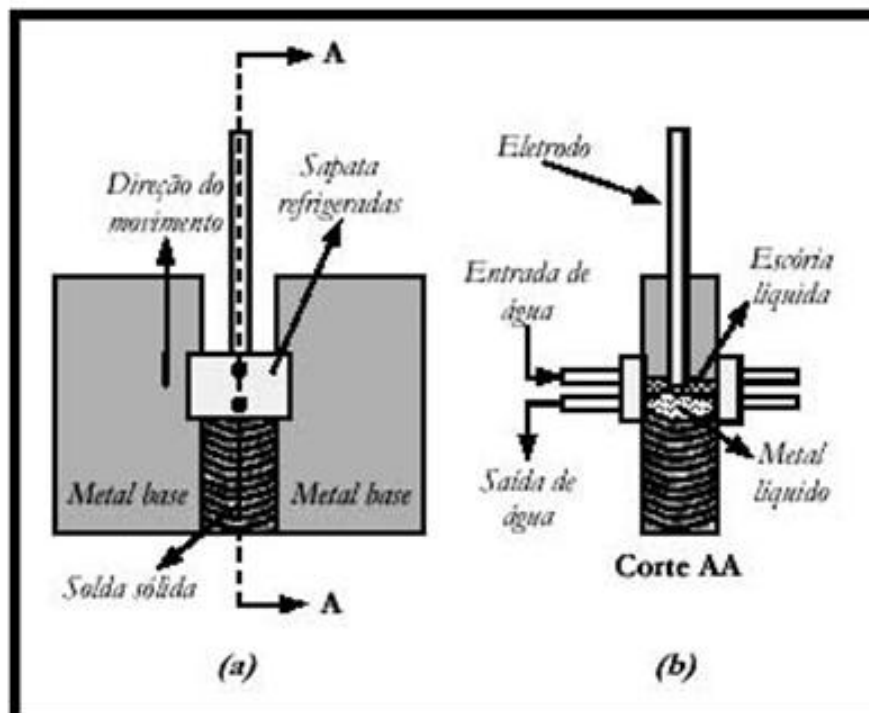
Esquema do processo de soldagem por eletroescória: (a) vista frontal e (b) seção transversal.
